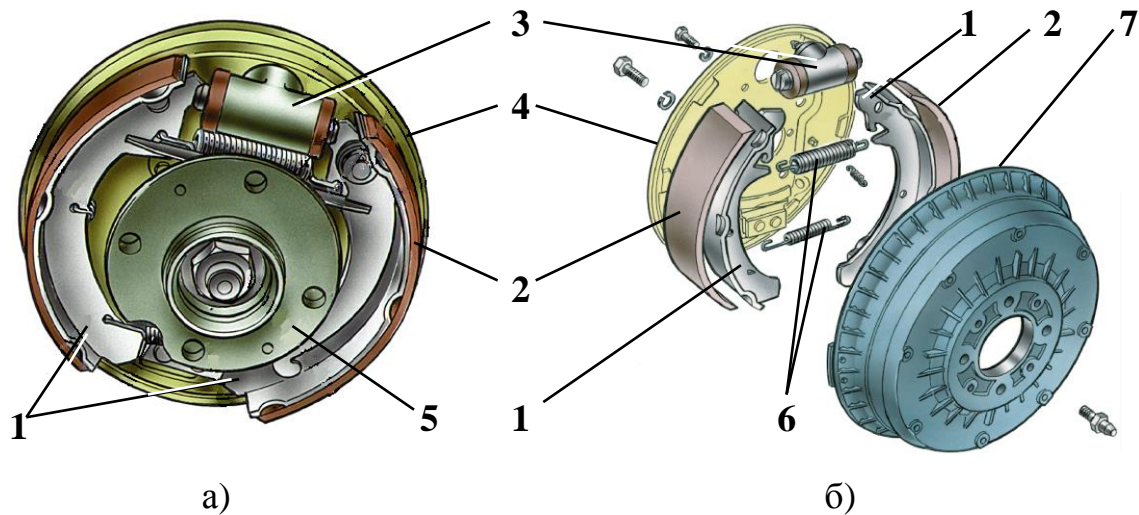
Конструкция барабанного тормозного механизма: а – неподвижные части, б – детали механизма; 1 – тормозные колодки, 2 – накладки тормозных колодок, 3 – разжимное устройство, 4 – опорный неподвижный диск тормозного механизма, 5 – фланец ступицы колеса, 6 – возвратные пружины, 7 – тормозной барабан
